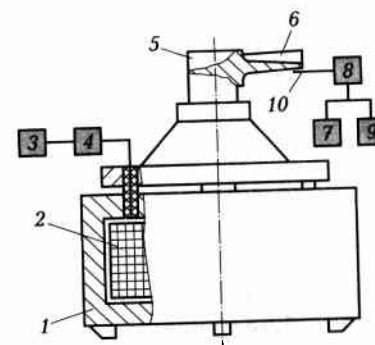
Схема определения частоты собственных колебаний детали: 1 — вибратор; 2 — катушка возбуждения; 3 — генератор сигналов; 4 — усилитель сигналов; 5 — приспособление для крепления проверяемой детали; 6 — проверяемая деталь; 7 — осциллограф; 8 — электронный усилитель; 9 — частотомер; 10 — емкостный первичный преобразователь сигнала
